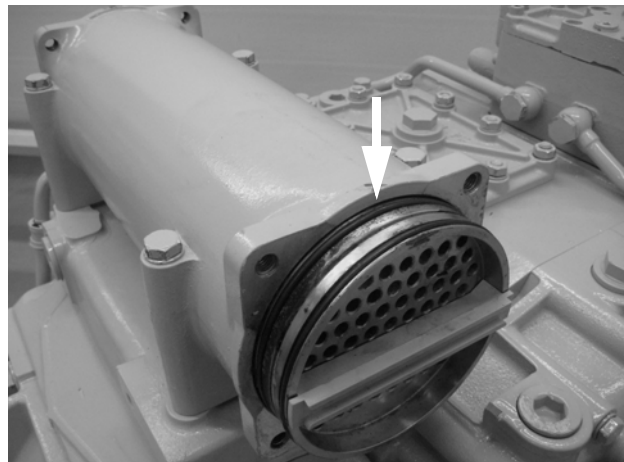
Auf den inneren O-Ring beim Einbau achten (Beispiel)
